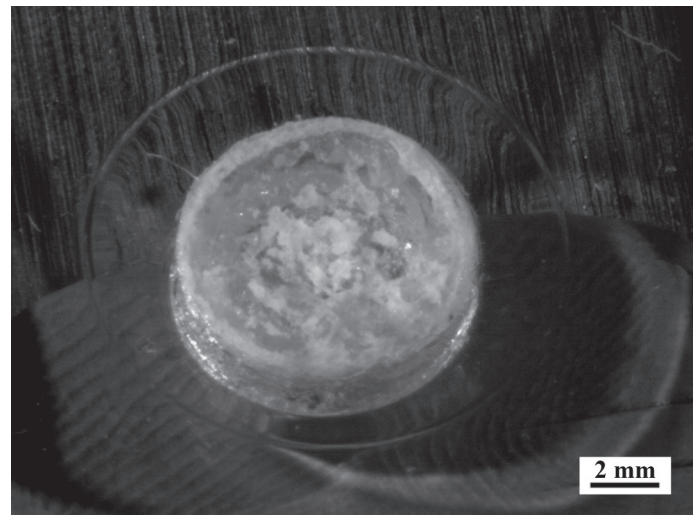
Superfície de amostra de PMMA soldada por FSpW.
